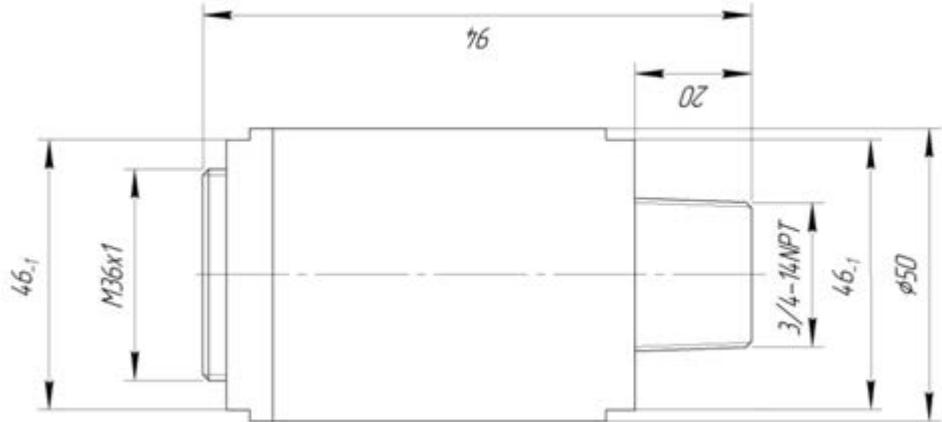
Габаритные размеры преобразователя газового универсального
